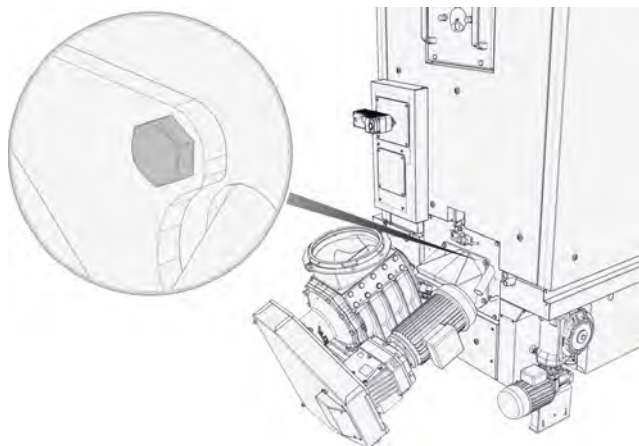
Joint d'étanchéité sur la bride de la vis d'alimentation
